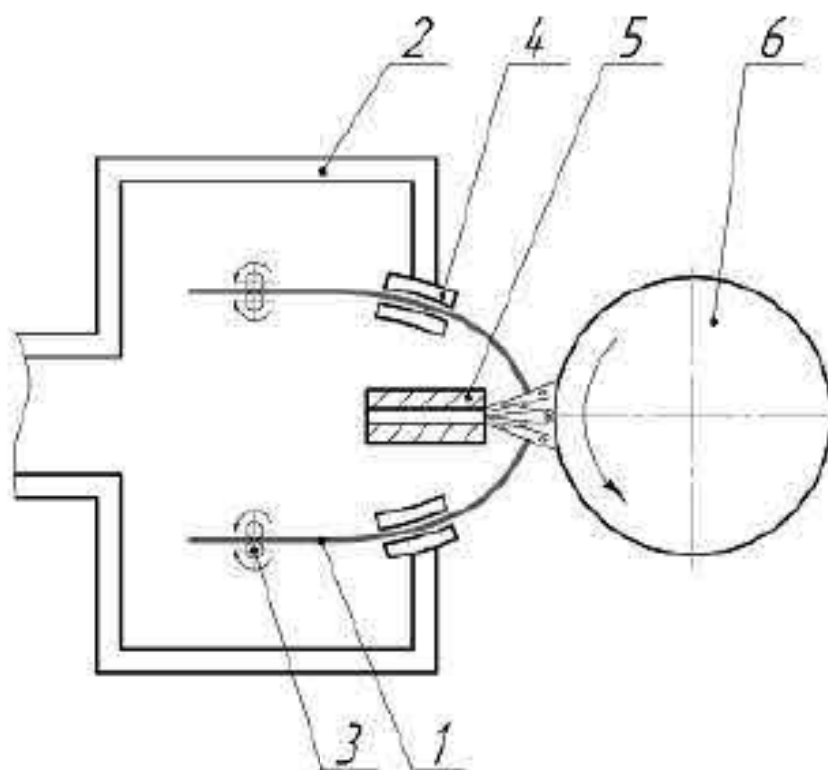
Металізатор: 1 – дріт, 2 – корпус, 3 – протилежні ролики, 4 – напрямна, 5 – насадка, 6 – деталь
